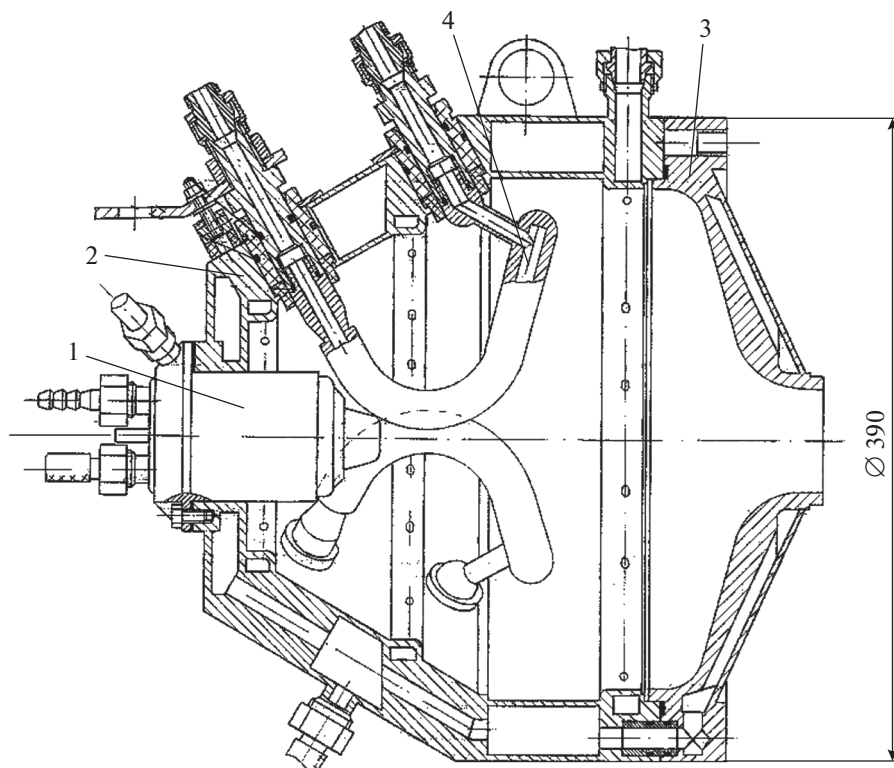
Высоковольтный трехфазный плазмотрон переменного тока: 1 – инжектор; 2 – корпус; 3 – сопло; 4 – электрод.
